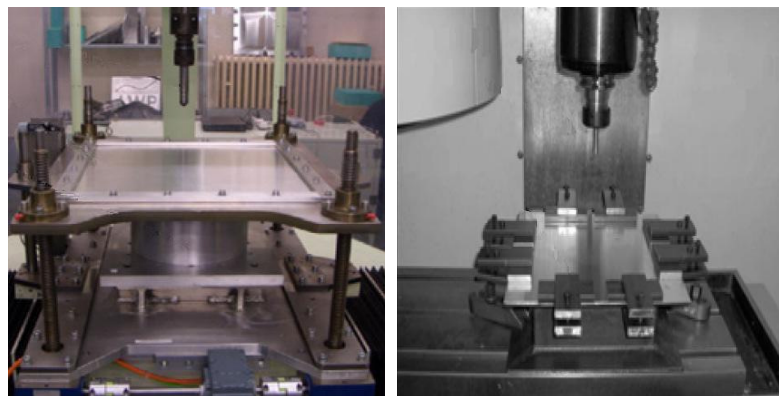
Máquinas-ferramenta adaptadas à estampagem incremental: fresadora de pórtico (esq.) [AER2009], e fresadora de consola (dir.) [DEJ2005].
